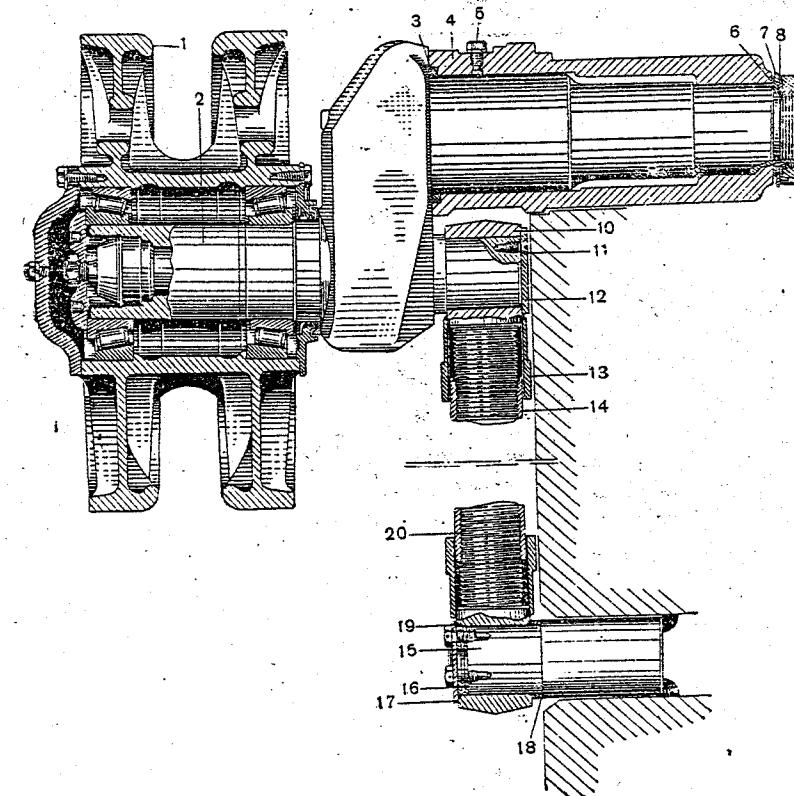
Направляющее колесо с натяжным механизмом (разрез):
